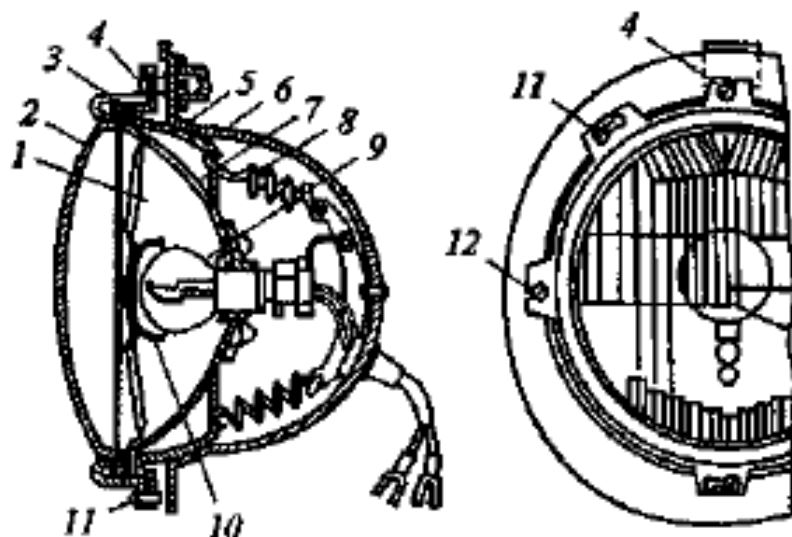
Фара автомобиля ВАЗ-2121: 1 – оптический элемент в сборе; 2 – рассеиватель; 3 – крепежный хомут (ободок); 4, 11 и 12 – винты; 5 – гнездо в кузове для установки фары; 6 – держатель; 7 – рефлектор; 8 – оттяжные пружины; 9 – лампа; 10 – экран
